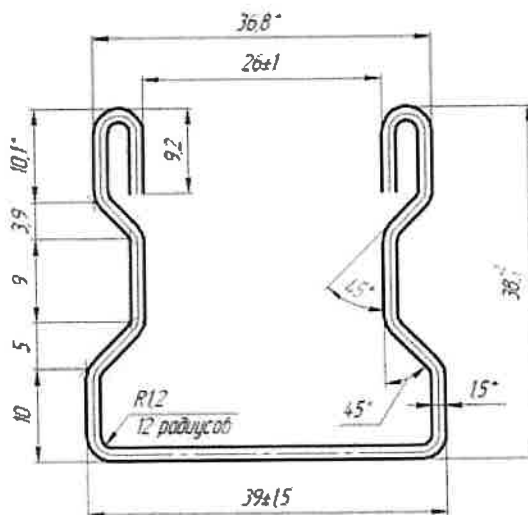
Профиль U-образный (размер заготовки 134,5 мм)
